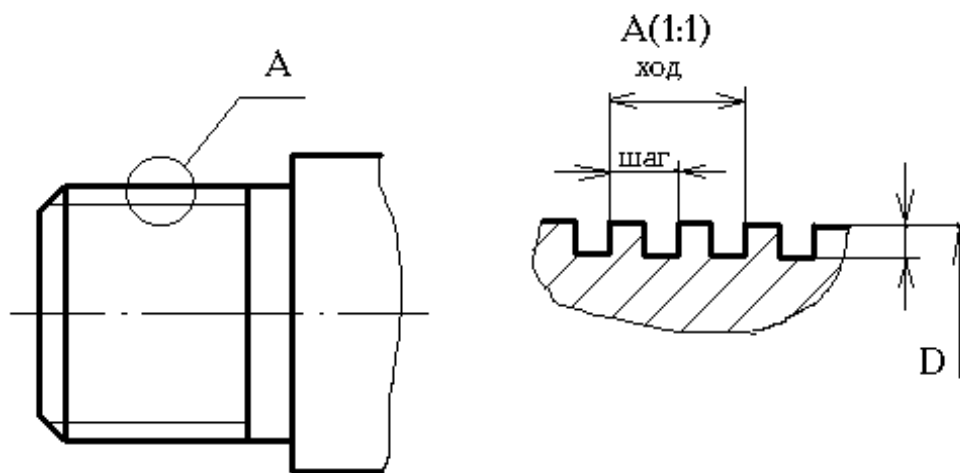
Пример изображения резьбы с нестандартным профилем
